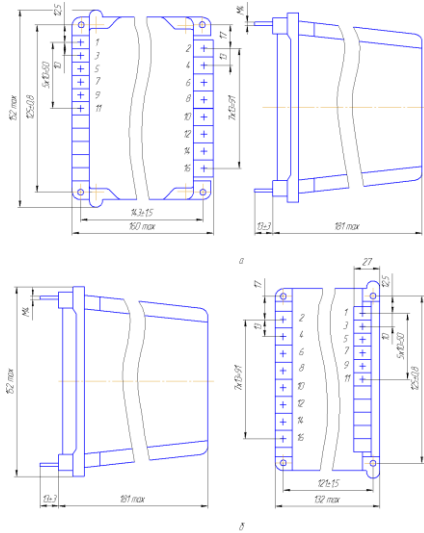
Габаритные, установочные, присоединительные размеры реле типа РСТ 23-6, приставки ПП11
